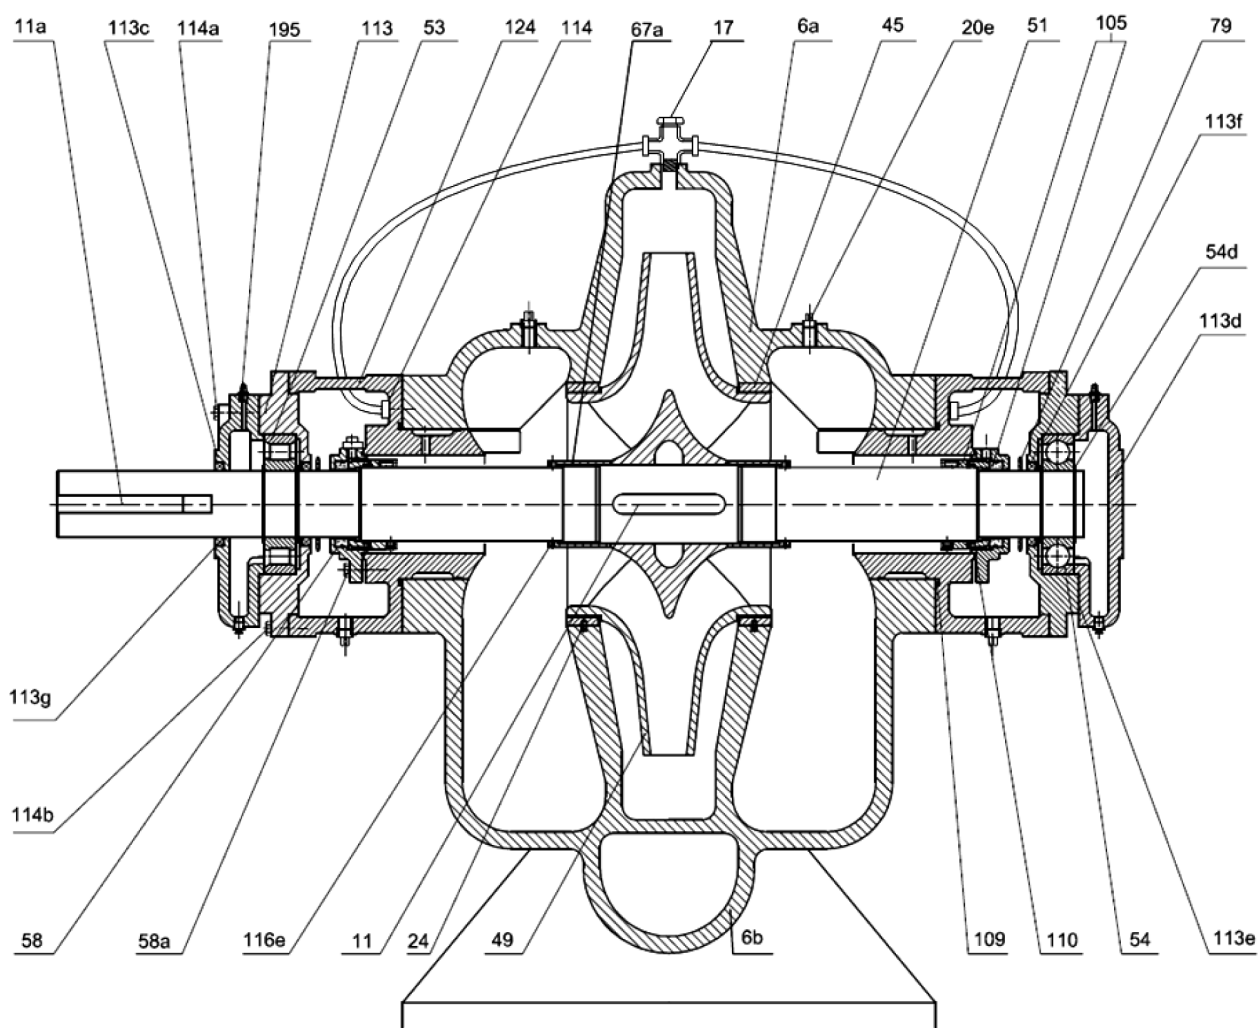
Вид в разрезе, тип конструкции 5, с торцевыми уплотнениями вала
